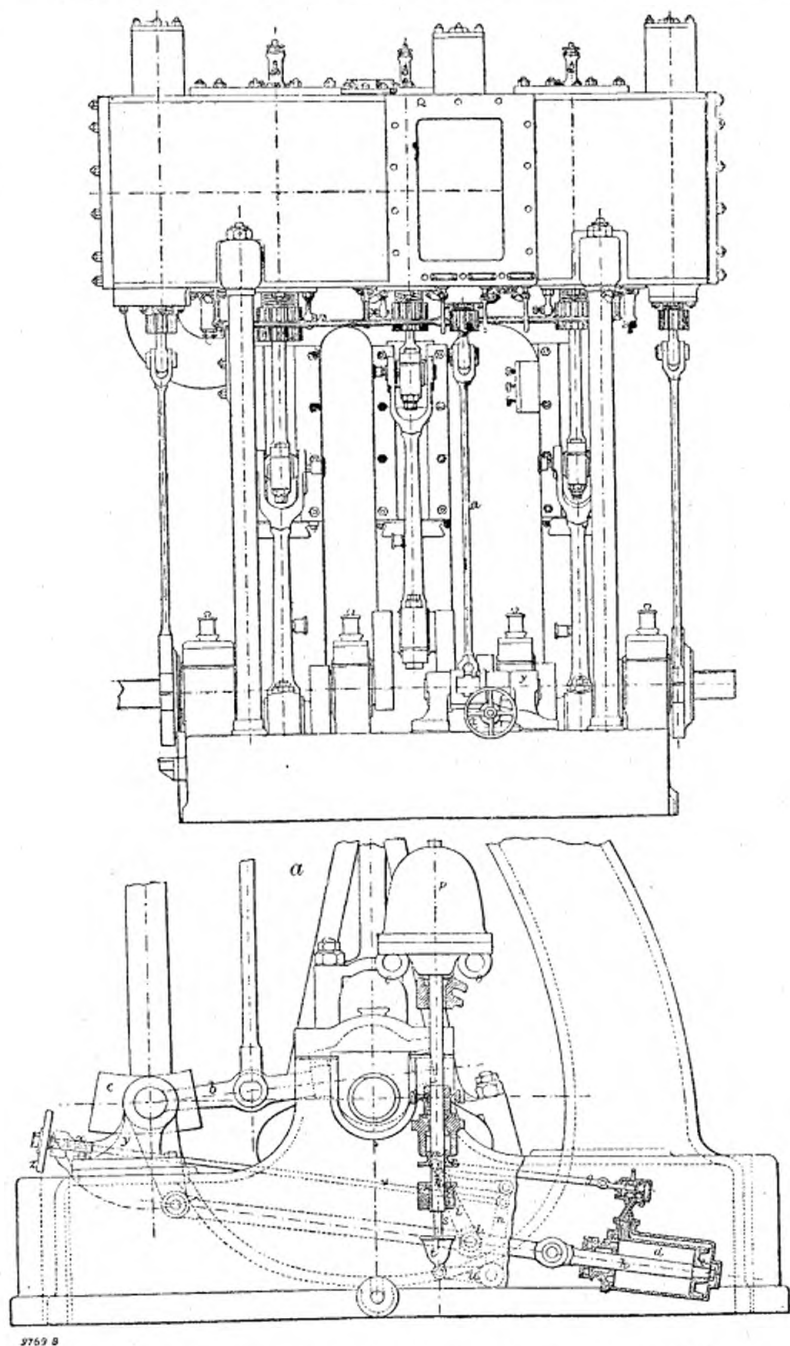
MACHINE FARCOT A TRIPLE EXPANSION
